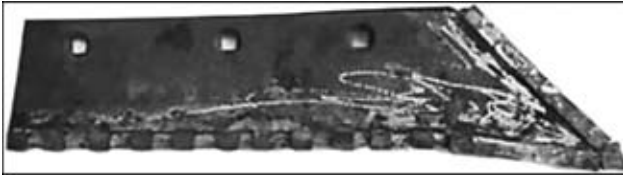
Общий вид упрочненного лемеха металлокерамическими пластинами [11]
